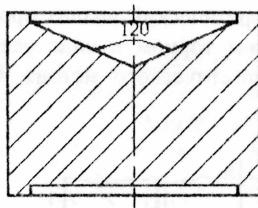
Профиль заготовок, подвергаемых сборке обратным выдавливанием
